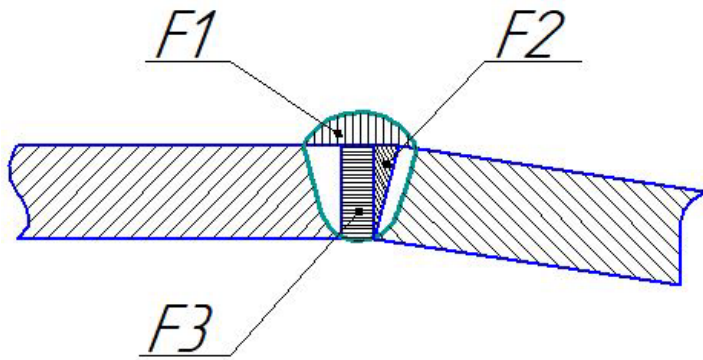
Ескіз площі наплавленого металу з'єднання У1 по ГОСТ 23518-79
